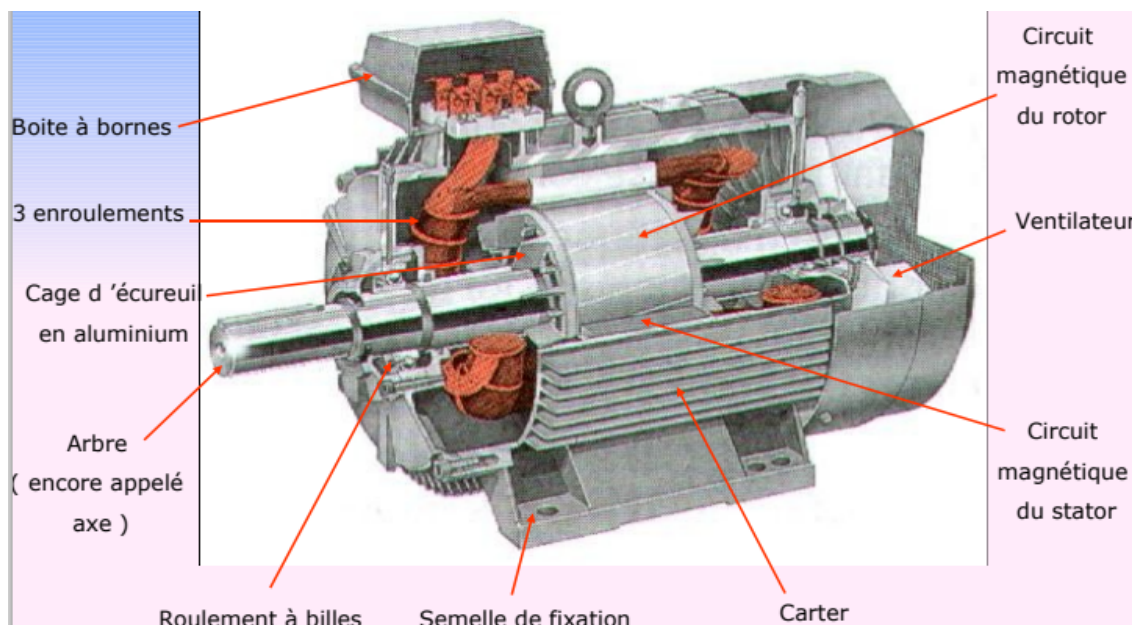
Vue Éclaté moteur asynchrone à cage d'écureuil
